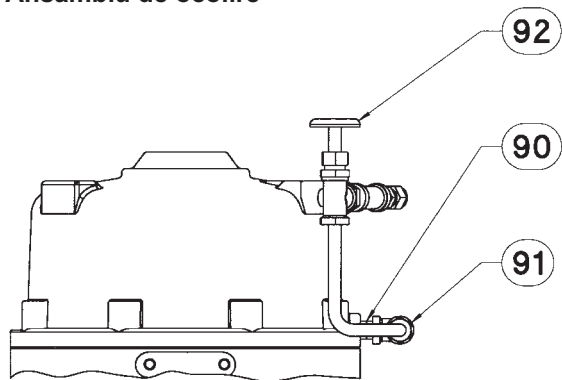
Actuator Fisher 585C dimensiune 60 cu cursă de 8 inci și dimensiune 68 cu cursă de 2, 4 și 8 inci
